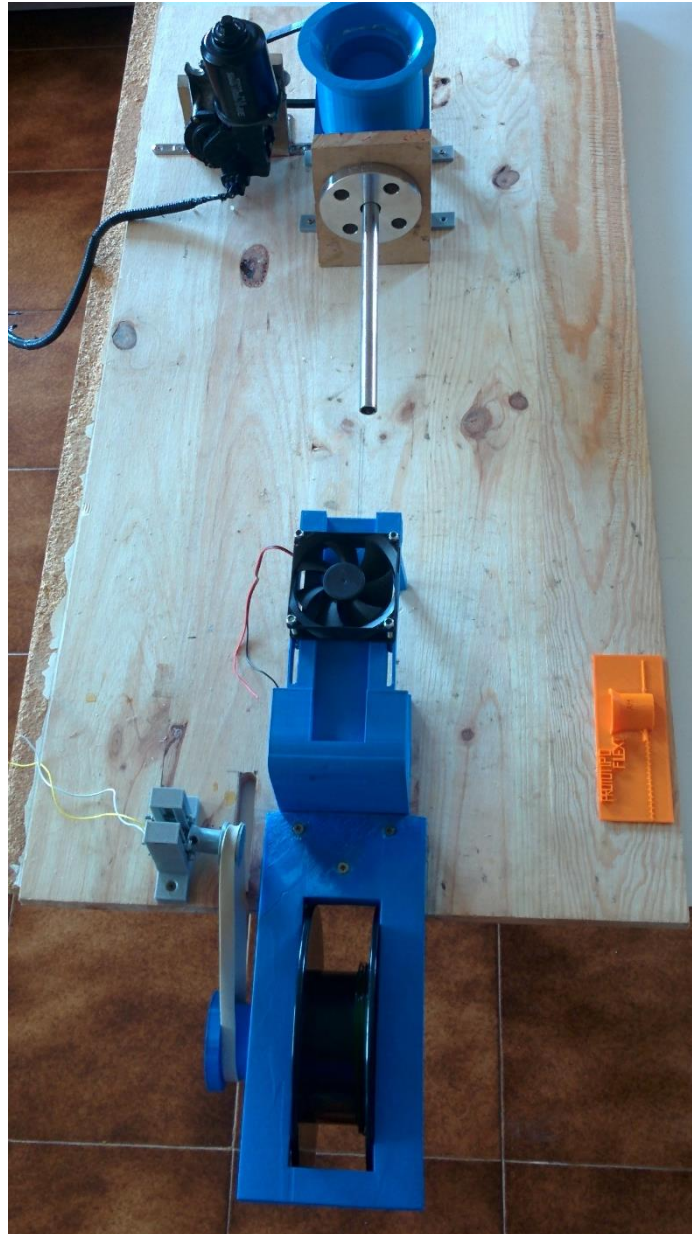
Montaje extrusora sin conexiones eléctricas. Fuente: Propia.
